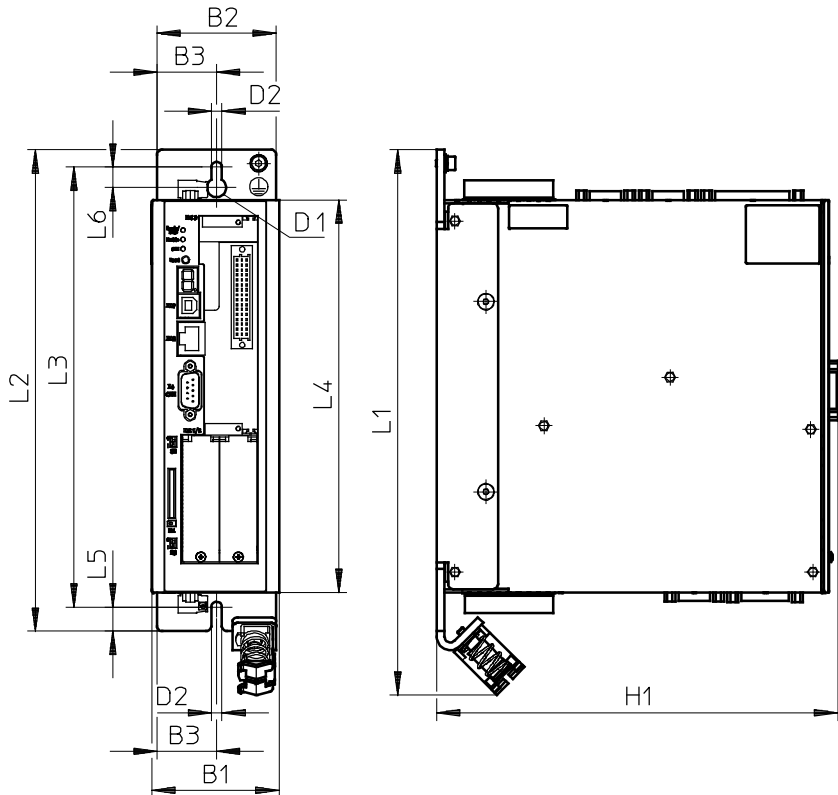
Motorcontroller CMMP-AS-...-M3: Montageplatte
